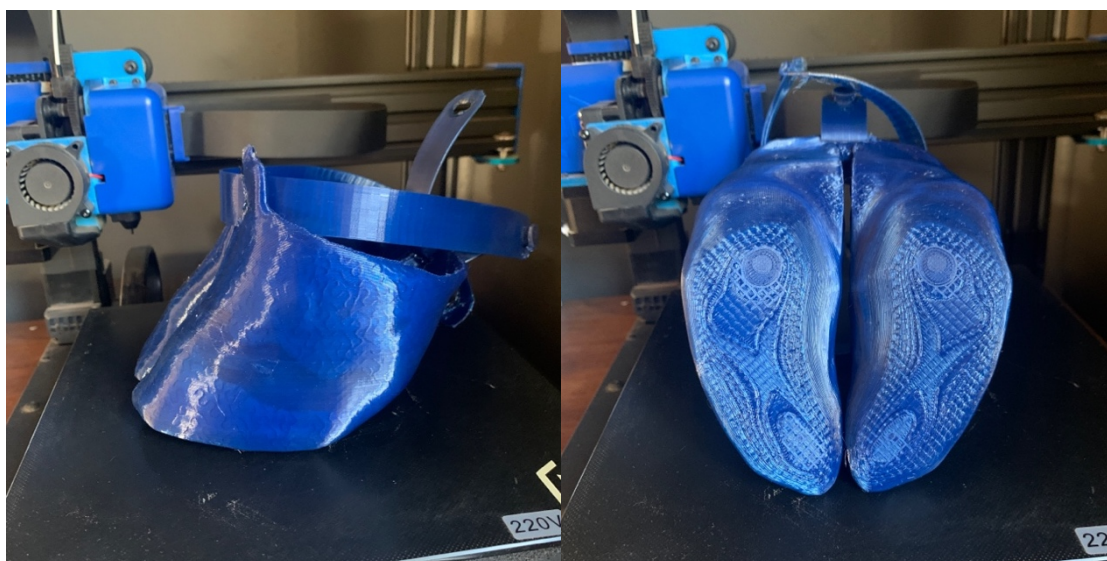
Prototipo de Moldura Impreso en MD Flex.
